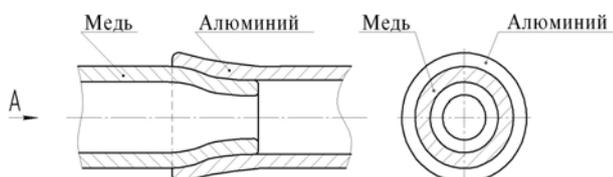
Телескопическое сварное соединение Cu-Al трубок
